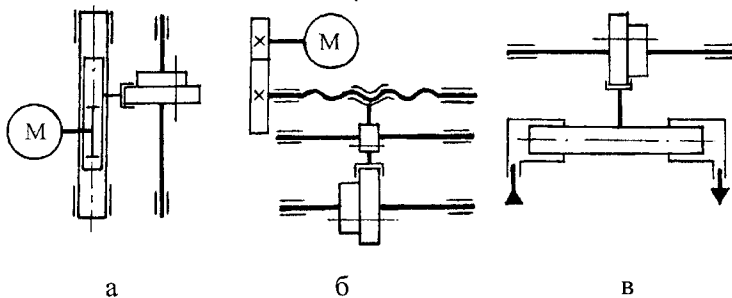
Схеми механізмів перемикання передач у верстатах з ЧПК: а – з рейкової передачі; б – з передачі гвинт-гайка; в – з гідроциліндром
